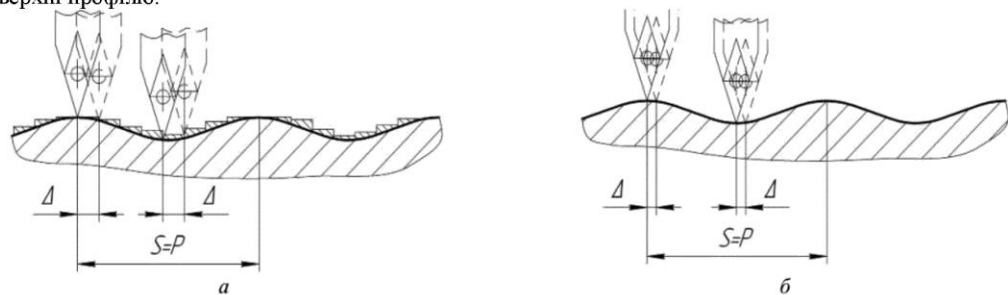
Схема зрізання припуску при точінні внутрішніх різьб стандартним різцем: а) чорнова обробка; б) чистова обробка
